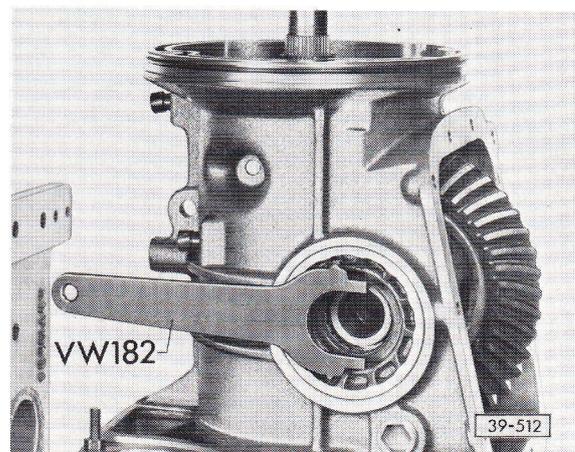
Bague de réglage de différentiel: dévisser ou visser
